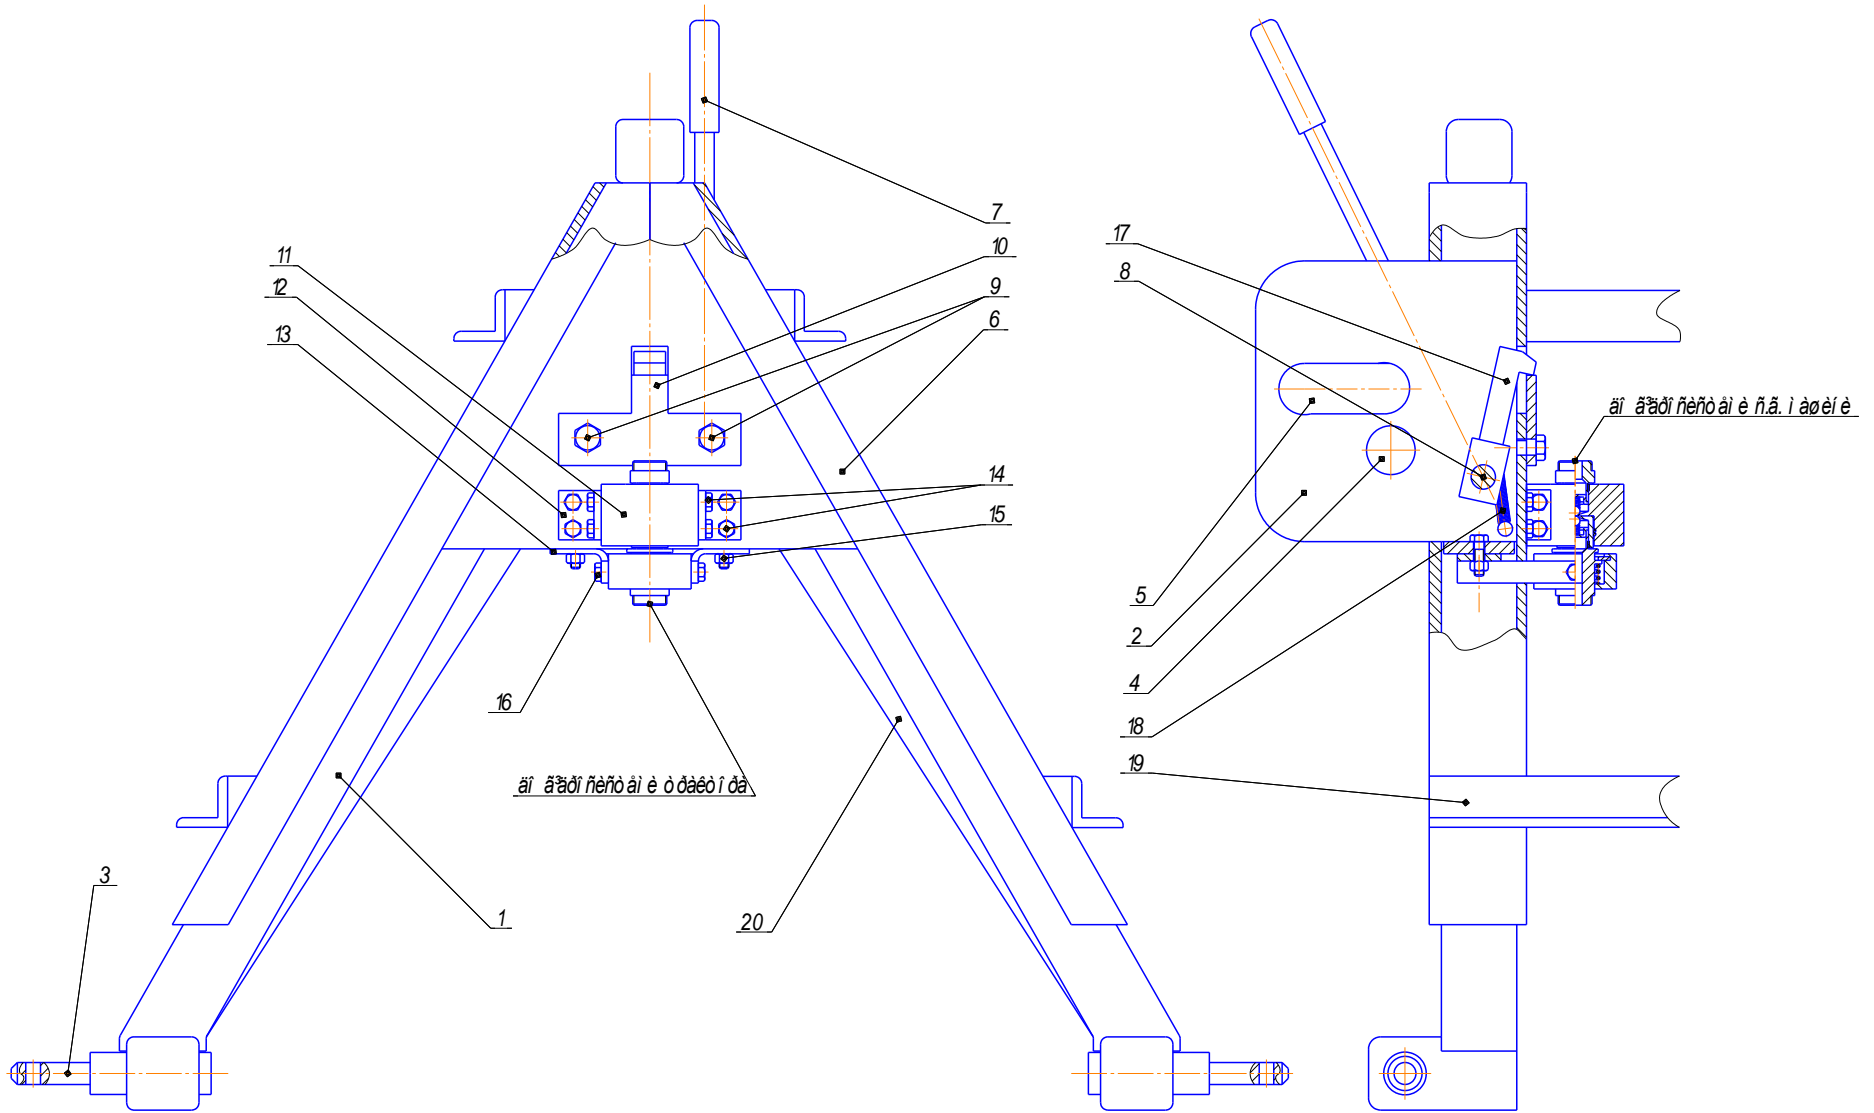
Гідрофікований автоматичний пристрій автозчипки
